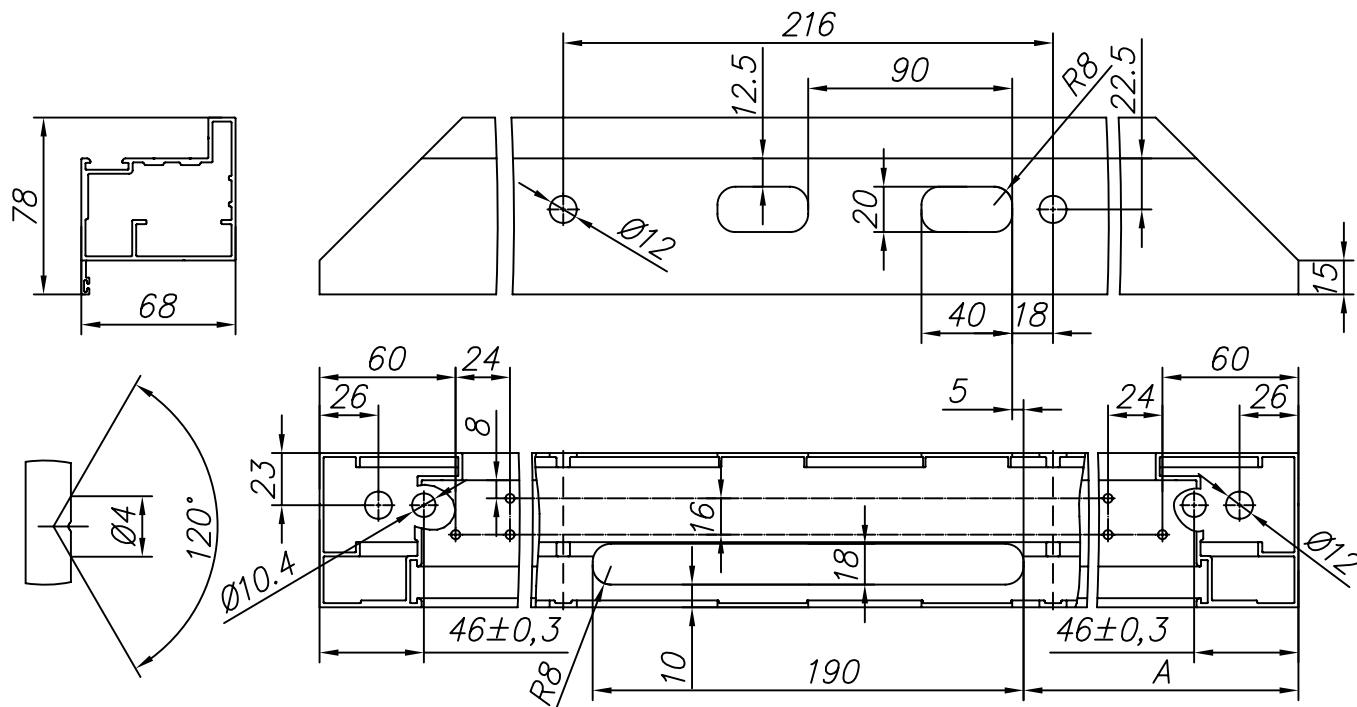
Изготовление стойки с пазом для замка из профиля FLGU.400.0110 (открытие внутрь, вправо)
